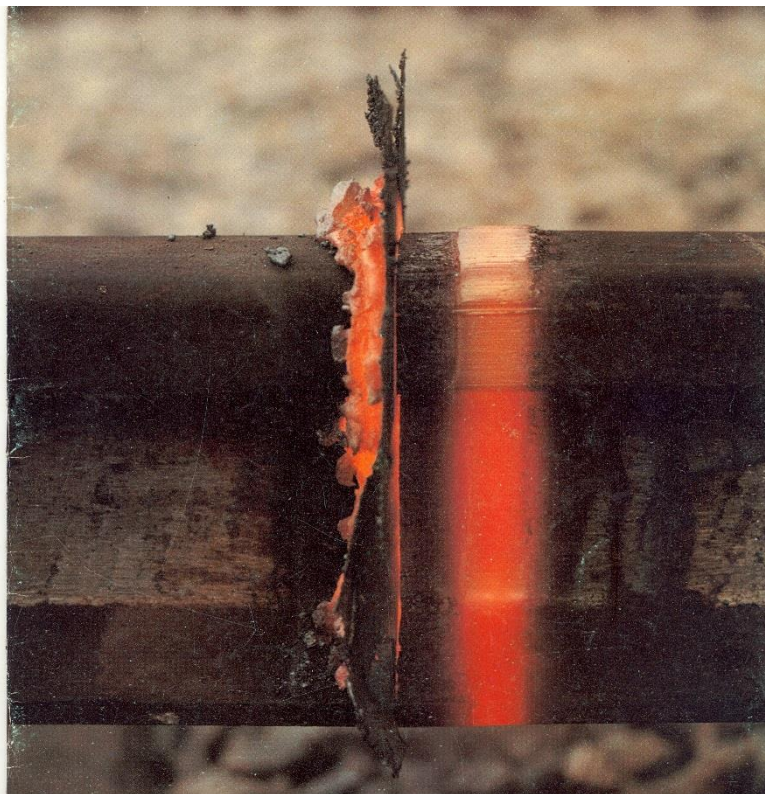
Вид ґрата після контактнo-стикового зварювання рейок.
